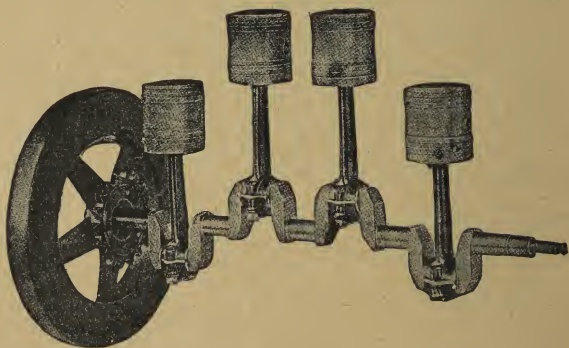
Kolben und Kurbelwelle mit fünfmaliger Lagerung.
